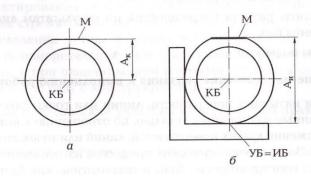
Простановка исходного размера: a — чертеж конструктора;  $\delta$  — выбор исходной базы (ИБ = УБ)
